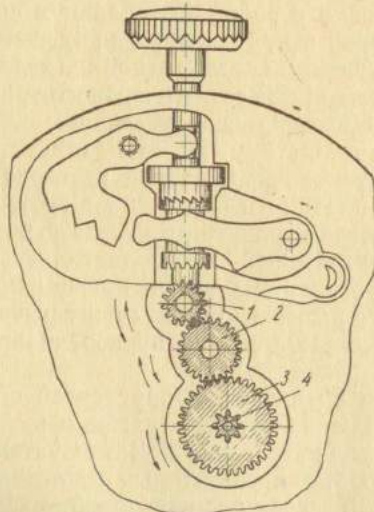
Сборка ключа, переводного рычага и кулачковой муфты.
